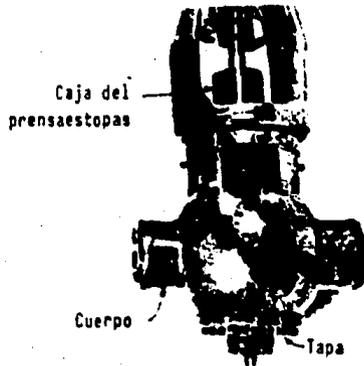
Válvula de control de cuerpo esférico y extremos soldables, con tapa en el fondo para su limpieza.
